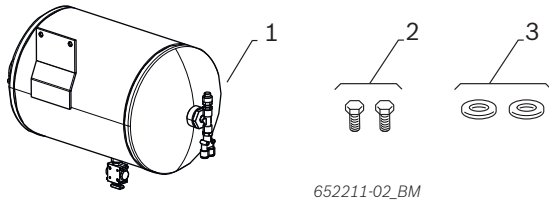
Accesorios para el montaje del recipiente de aire comprimido
